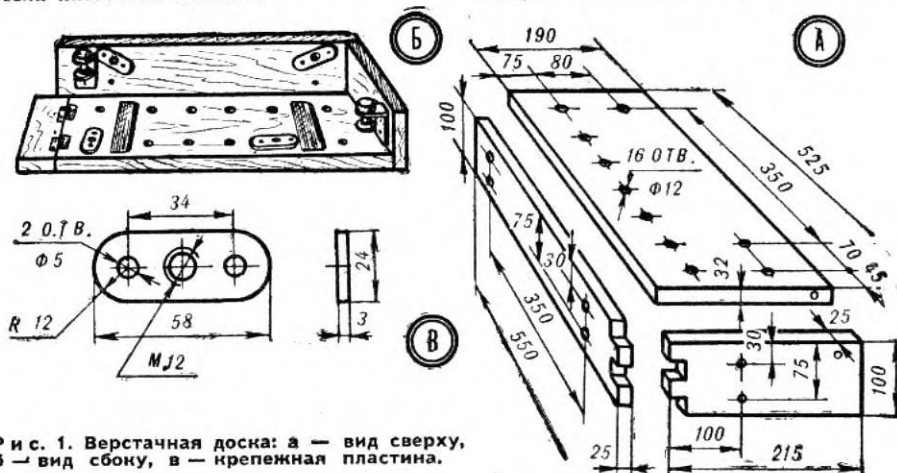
Верстачная доска: а — вид сверху, б — вид сбоку, в — крепежная пластина.
